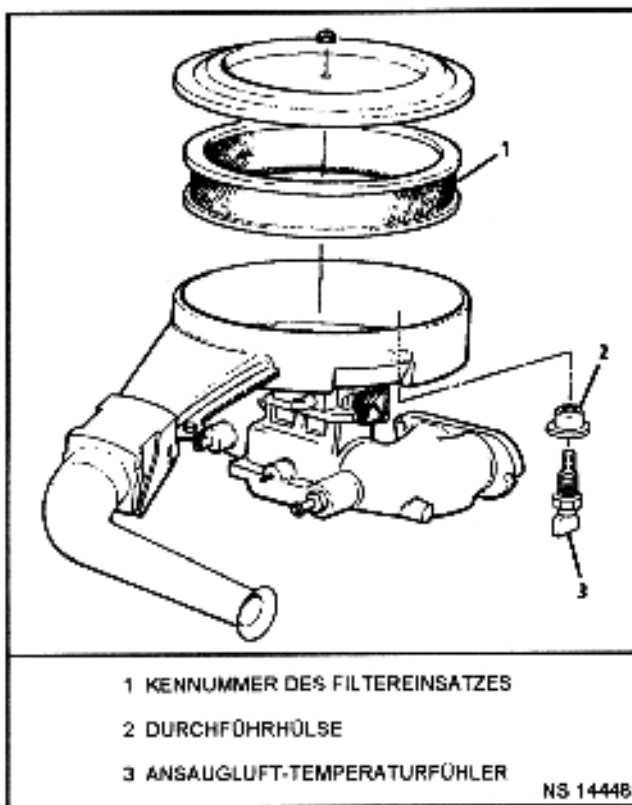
Einbaulage - Ansaugluft-Temperaturfühler
